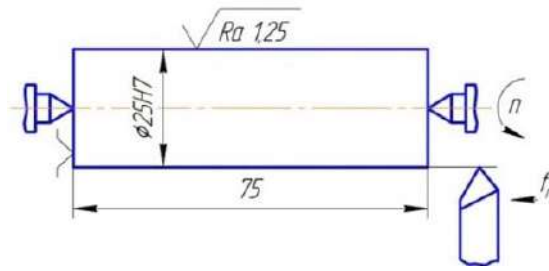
Схема обработки детали из закалённой стали (55HRC) резцом, оснащенным пластиной из кубического нитрида бора
